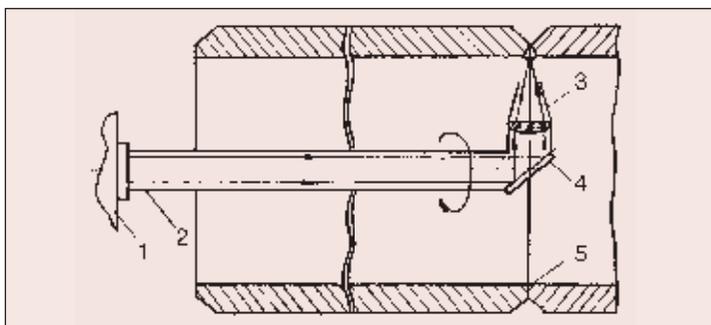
Схема орбитальной сварки корневого шва для монтажа трубных стыков: 1 — CO₂-лазер; 2 — поворотный лучепровод; 3 — лазерная сварочная головка; 4 — поворотное зеркало; 5 — неповоротный трубный стык
